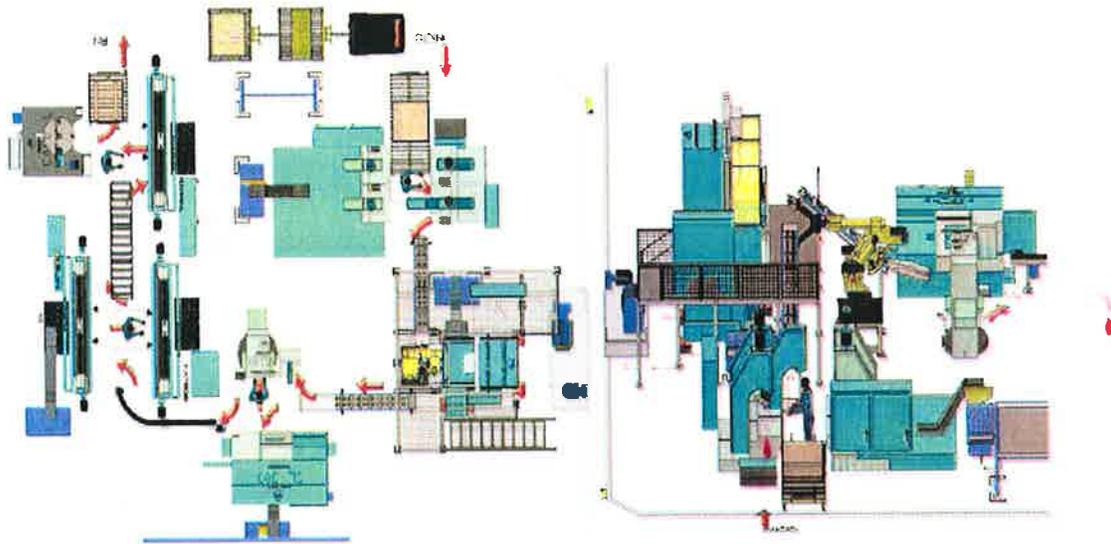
Propuesta de LayOut (vista superior y vista frontal) (ANEXO C)
